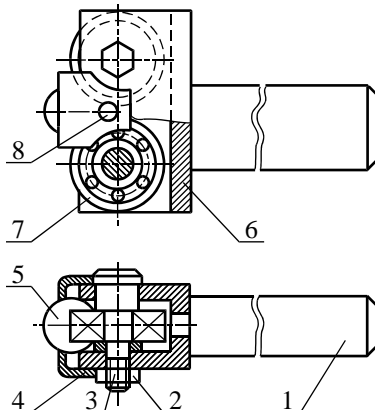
Кулькова жорстка накатка та її встановлення у різцетримачі токарного верстата: 1 – державка; 2 – гайка; 3 – центрувальний гвинт; 4 – сепаратор; 5 – кулька (деформуючий елемент); 6 – корпус; 7 – шарикопідшипник; 8 – обойма кульки
